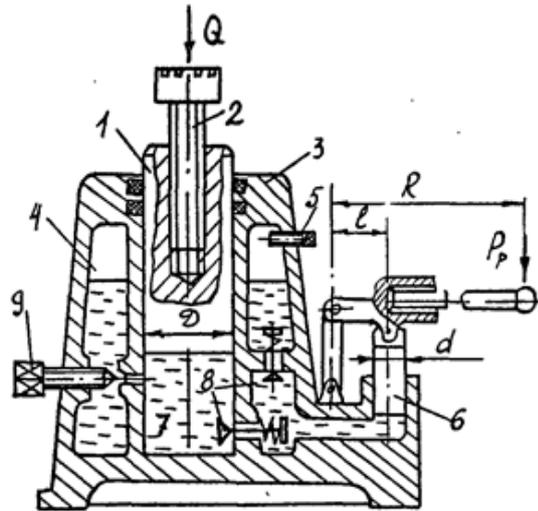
Розрахункова схема гідравлічного домкрата: 1 – шток; 2 – гвинт; 3 – корпус; 4 – порожнина; 5 – пробка; 6 – насос; 7 – порожнина під штоком; 8 – клапан; 9 – кран.
